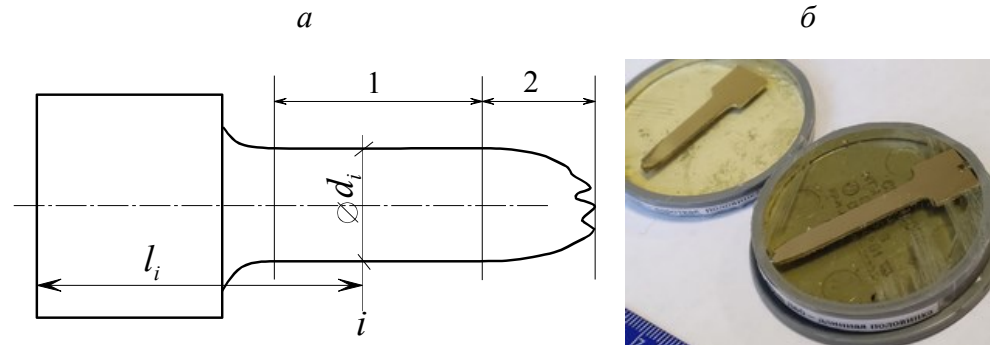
Схема обмера половинок разорванного образца (а) и шлифы двух половинок образца из латуни Л60 (б): 1 — зона равномерной деформации образца; 2 — зона шейки
